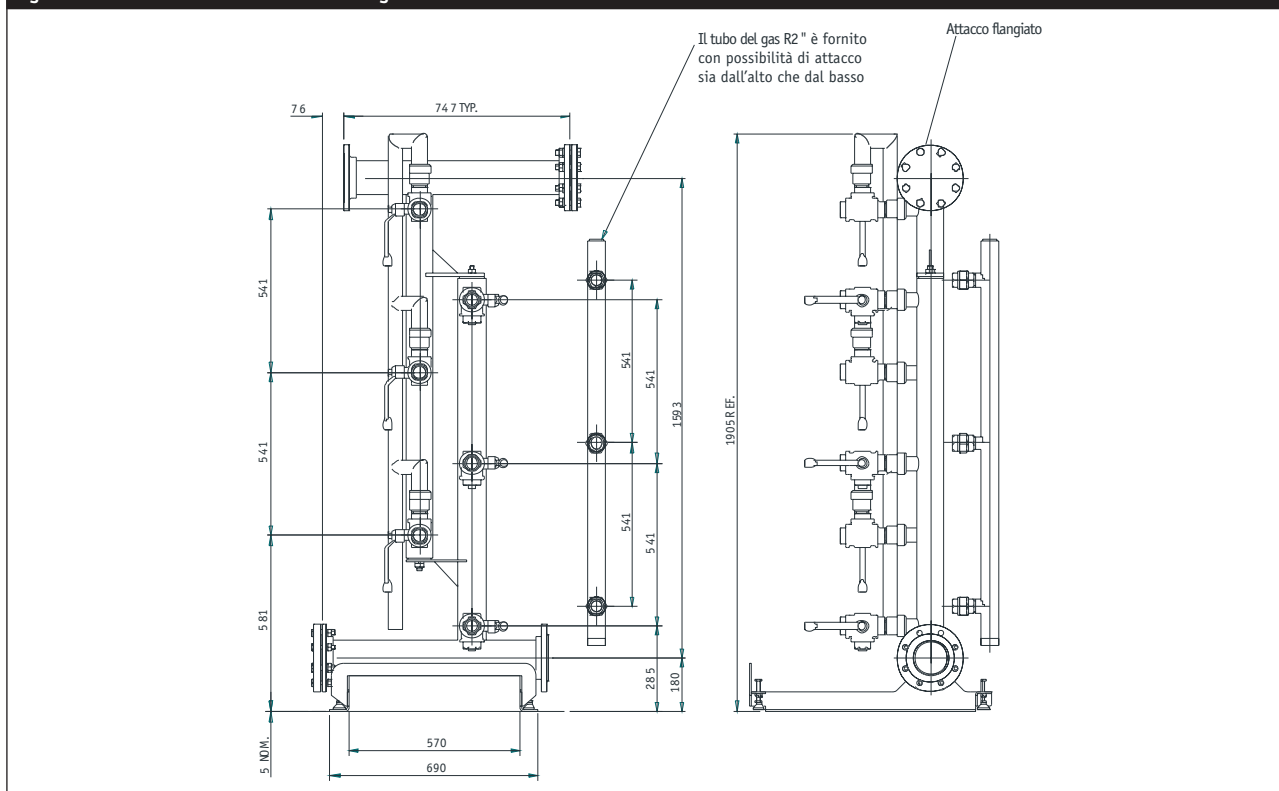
Dimensione attacchi MultiBongas.eco 300-3x100 - 345 -3x115
